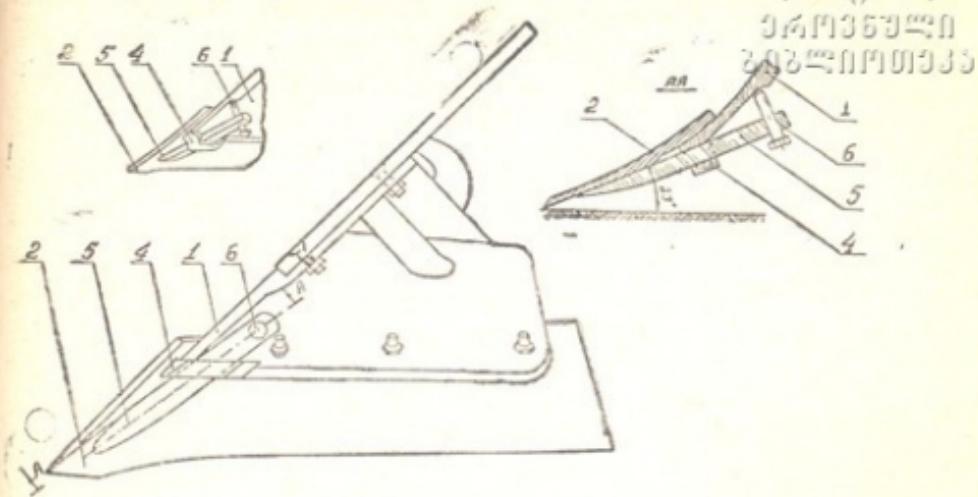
Плужный корпус; а — общий вид; б — разрез А-А; в — часть плужного корпуса, вид снизу.
